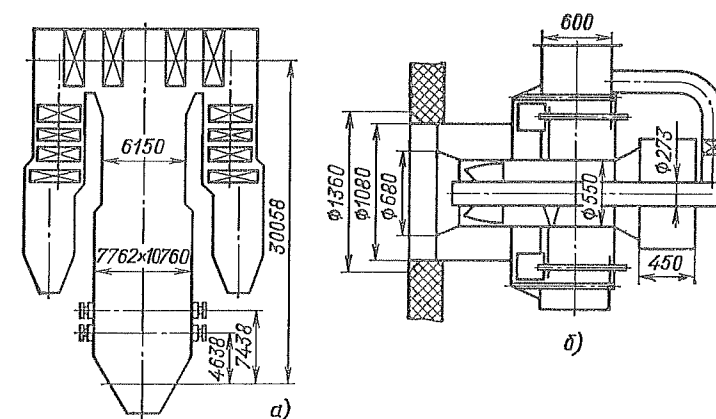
Схемы топочной камеры (а) и горелочного устройства (б) котла ПК-39-2 4
